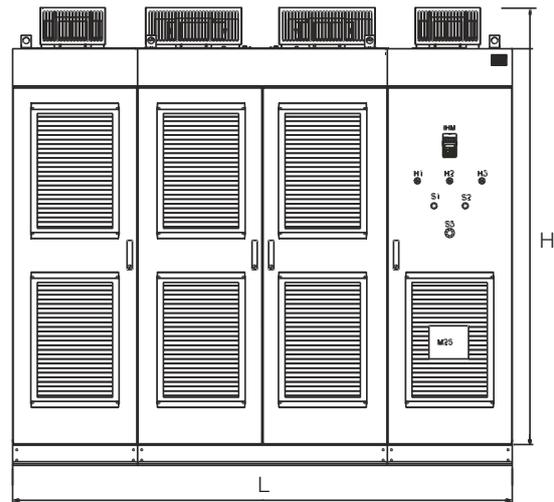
Dimensions du panneau de MVW-01 complet (en mm)
